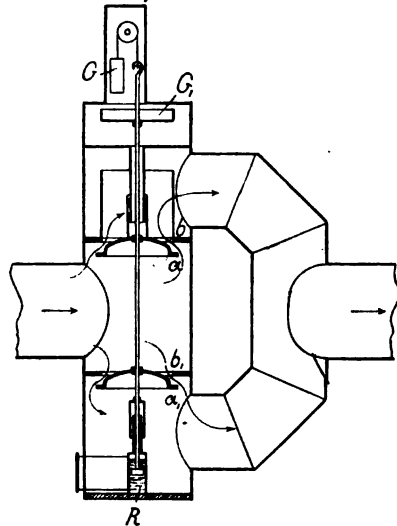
Druckregler für Heizgas. Das Gas strömt von links ein. Wird sein Druck größer, so heben sich die Ventilteller und verengen den Querschnitt. Fällt der Druck, so sinken die Ventilteller und lassen größeren Querschnitt frei. Voraussetzung für gute Wirksamkeit ist, daß die Gewichte gut ausgeglichen sind und eine Bremsung durch einen Wasserkolben geschaffen ist, damit nicht ein fortwährendes Hin- und Herpendeln geschieht.
